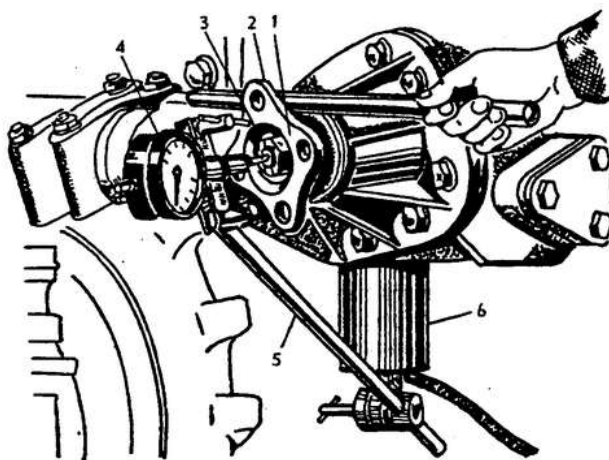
Измерение осевого зазора в подшипниках шестерни главной передачи переднего ведущего моста: 1 – фланец стакана ведущей шестерни; 2 – ломик; 3 – шток приспособления; 4 – индикатор; 5 – штатив; 6 – электромагнит
